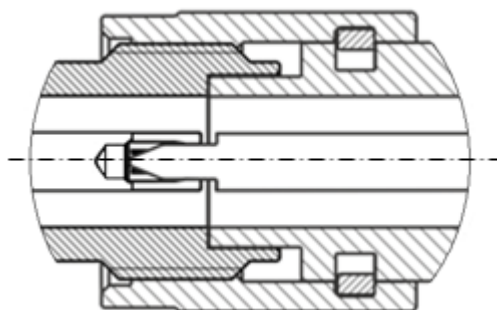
Соединители тип 3,5 мм (розетка слева, вилка справа)
